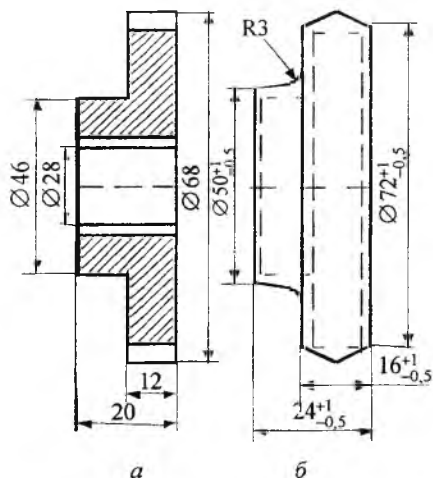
К примеру нормативного расчета размеров штампованной заготовки: а – эскиз детали; б – эскиз штамповки
